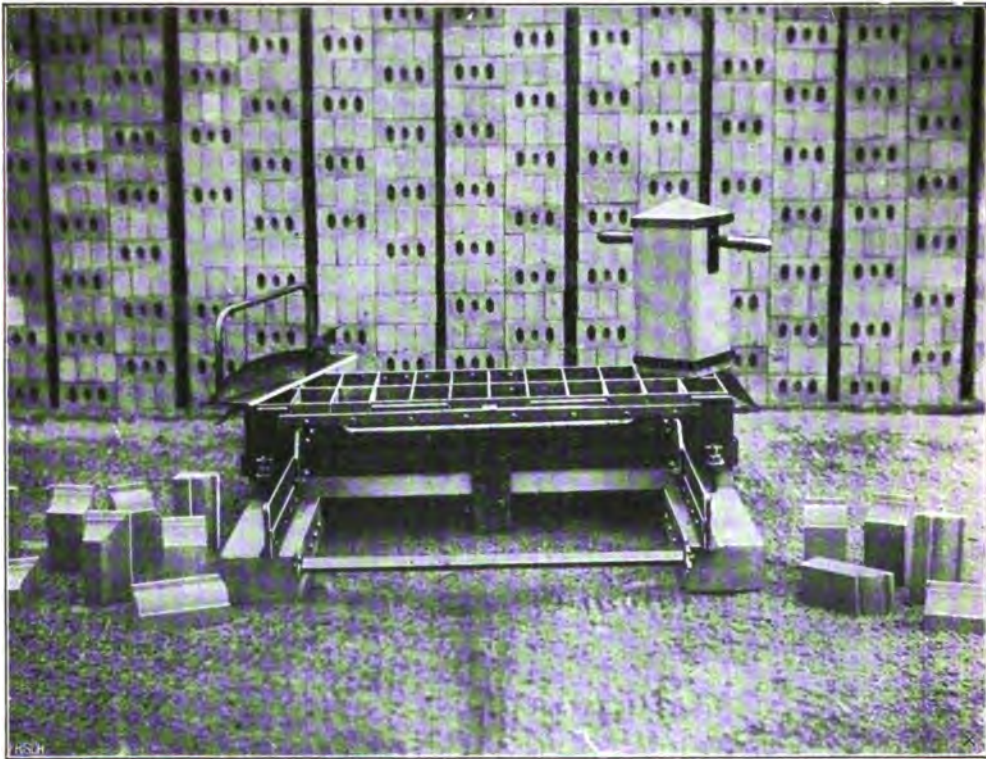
Zementmauersteinmaschine „Der kleine Handwerker“
